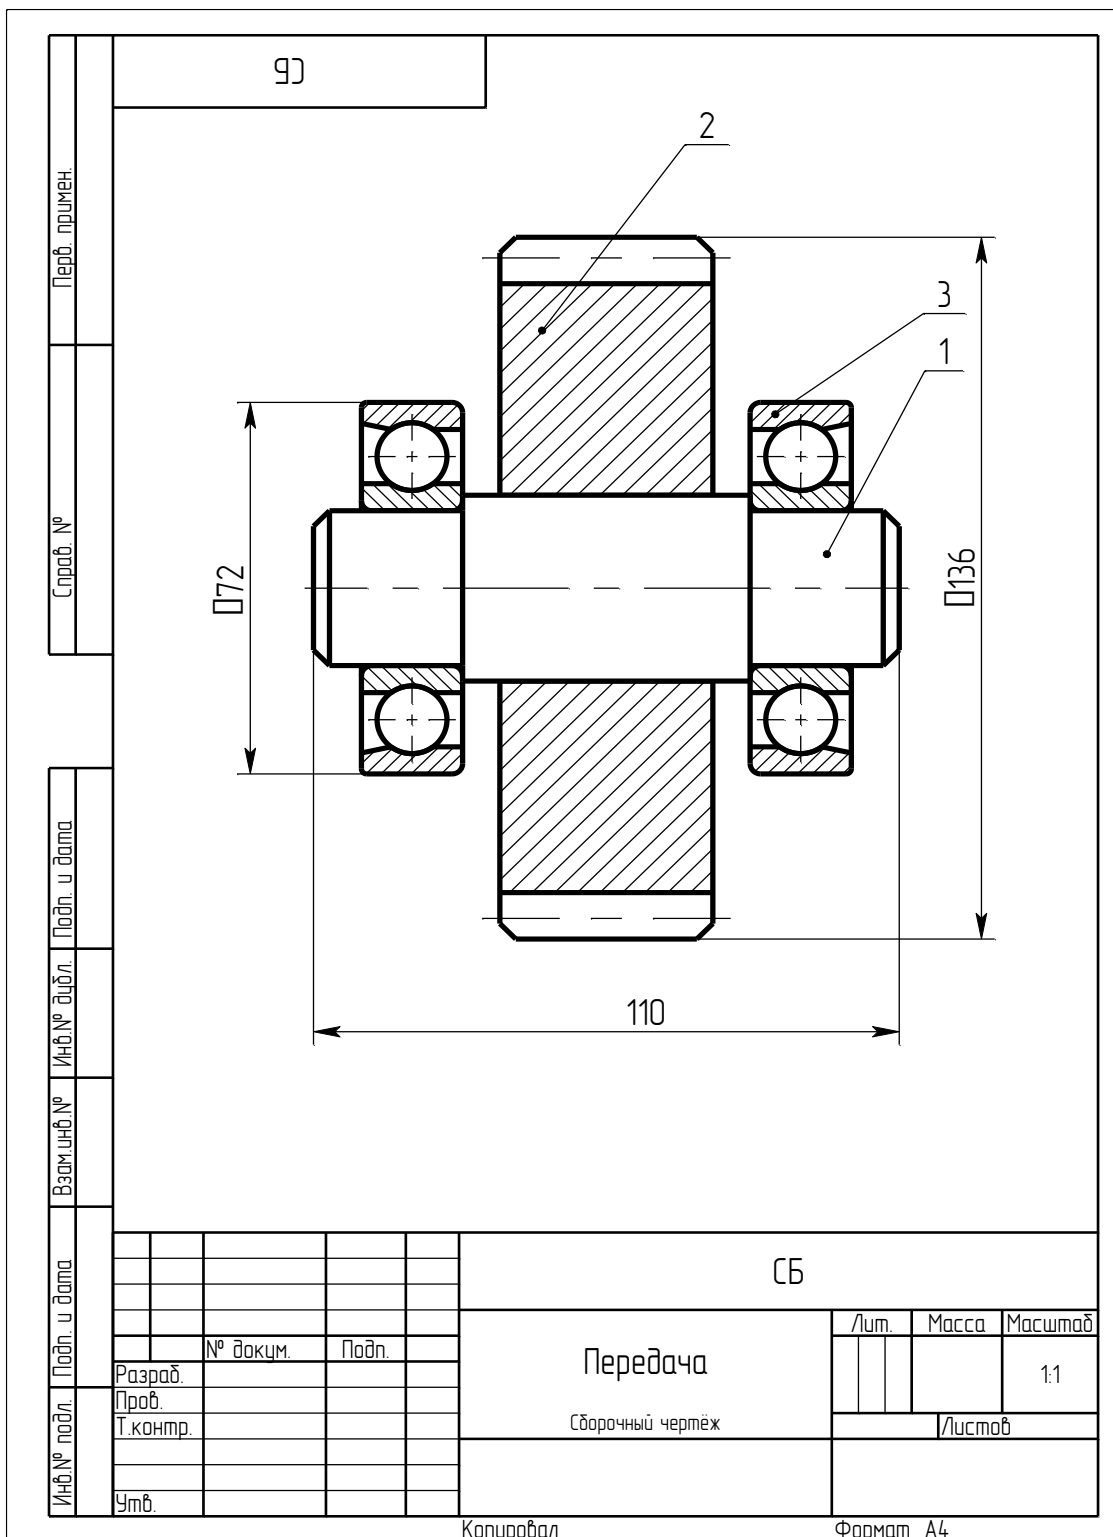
Сборочный чертеж в T-FLEX CAD
